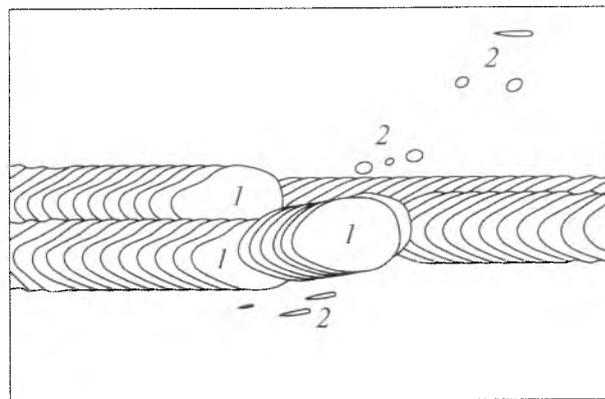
Кратеры 1 на участках окончания валиков шва стыкового сварного соединения обечайки сосуда. Некоторые из кратеров частично перекрыты наплавленным металлом. В околошовной зоне с обеих сторон шва наблюдаются забоины 2. Ширина валика порядка 10 мм
